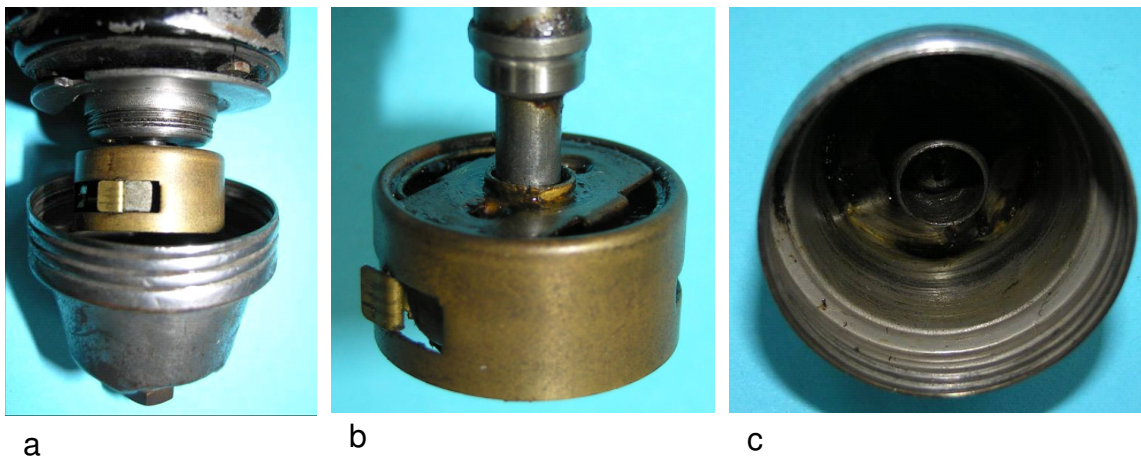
Schalter: a) Schalterkappe, Schalter und Blechteller, b) Schalter unterhalb des Lagersitzes auf der Welle eingerastet, c) Schalterkappe mit dem innen liegenden Schleifring
